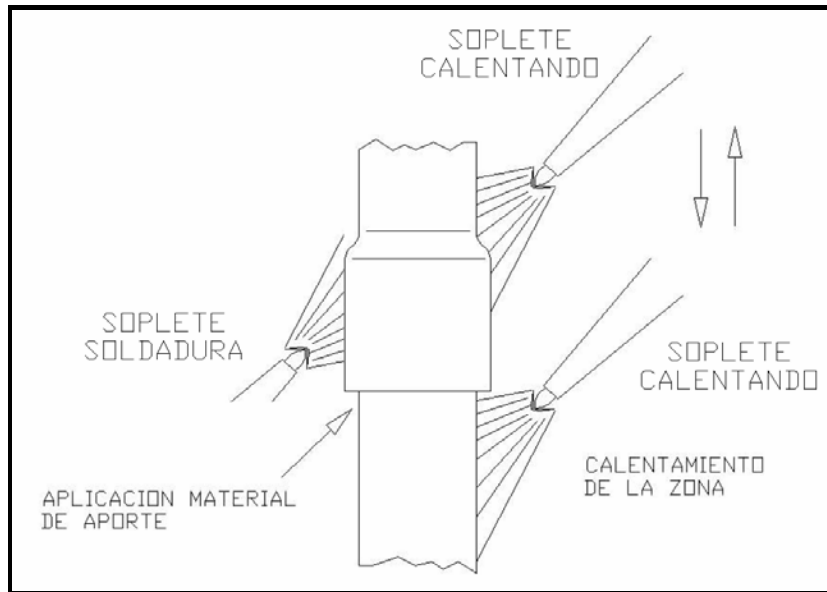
Posiciones del soplete durante la soldadura
